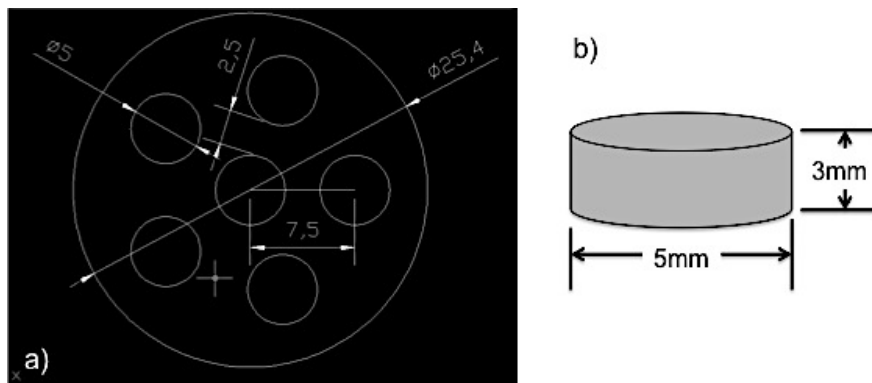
2 Dimensiones del material de experimentación. a) vista superior de la barra de H282, dimensiones en mm. b) muestras para experimentación.
